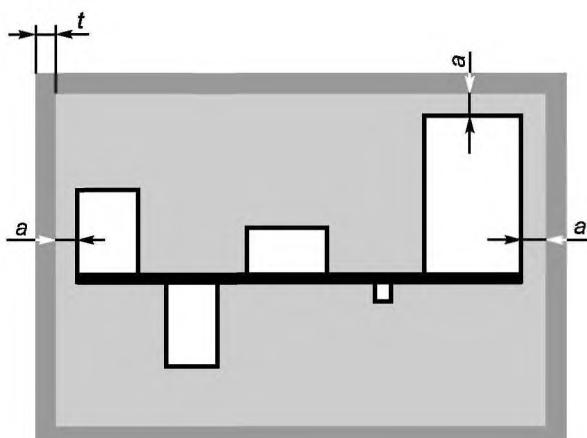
Расстояния между стенкой или открытой поверхностью компаунда и элементами или проводниками
